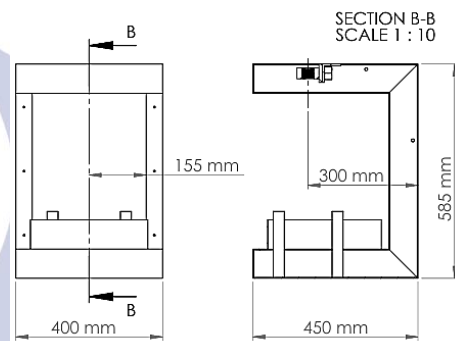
Dimensi Rangka Mesin Presstechno S01
